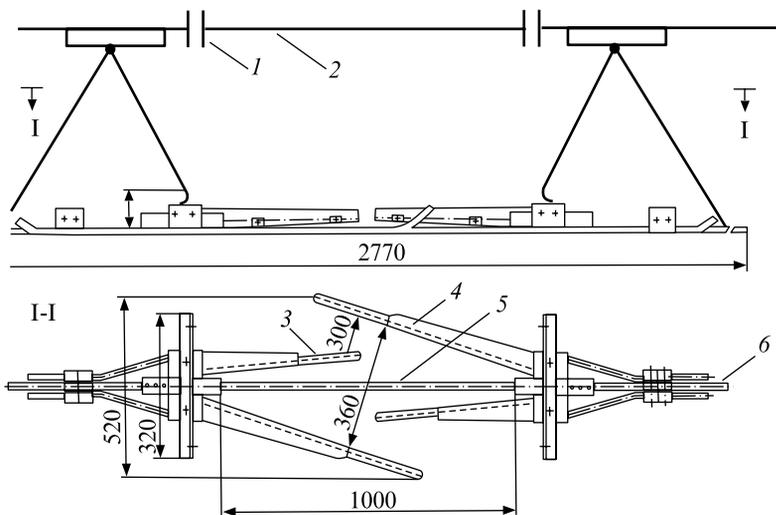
Секционный изолятор переменного тока ИС-0-80-25/3: 1 — изолятор; 2 — штанга; 3 и 4 — короткий и длинный скользящие; 5 — изолятор натяжной полимерной гладкостержневой НСФ-120-25/1,1 (1,2); 6 — контактный провод
